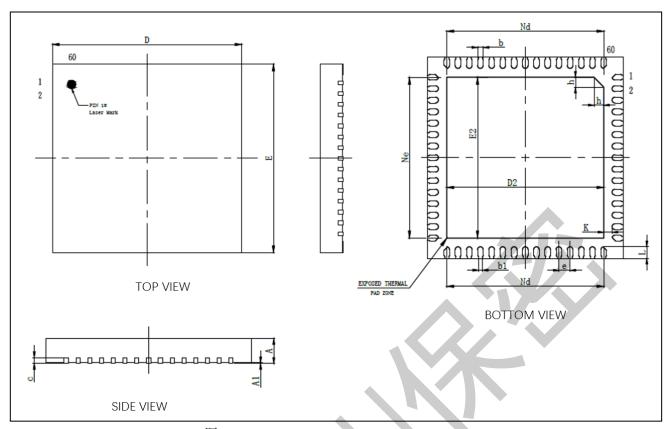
QFN60L7 x 7 mm 60-pin package outline
